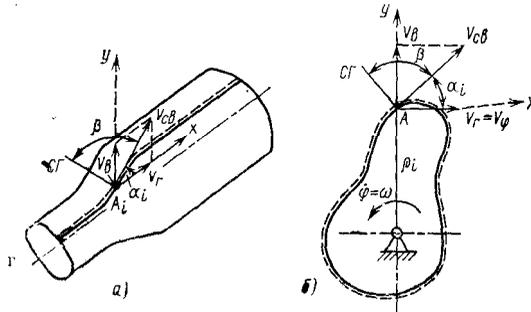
Перемещения сварочной горелки при сварке деталей с криволинейной образующей в вертикальной плоскости:
